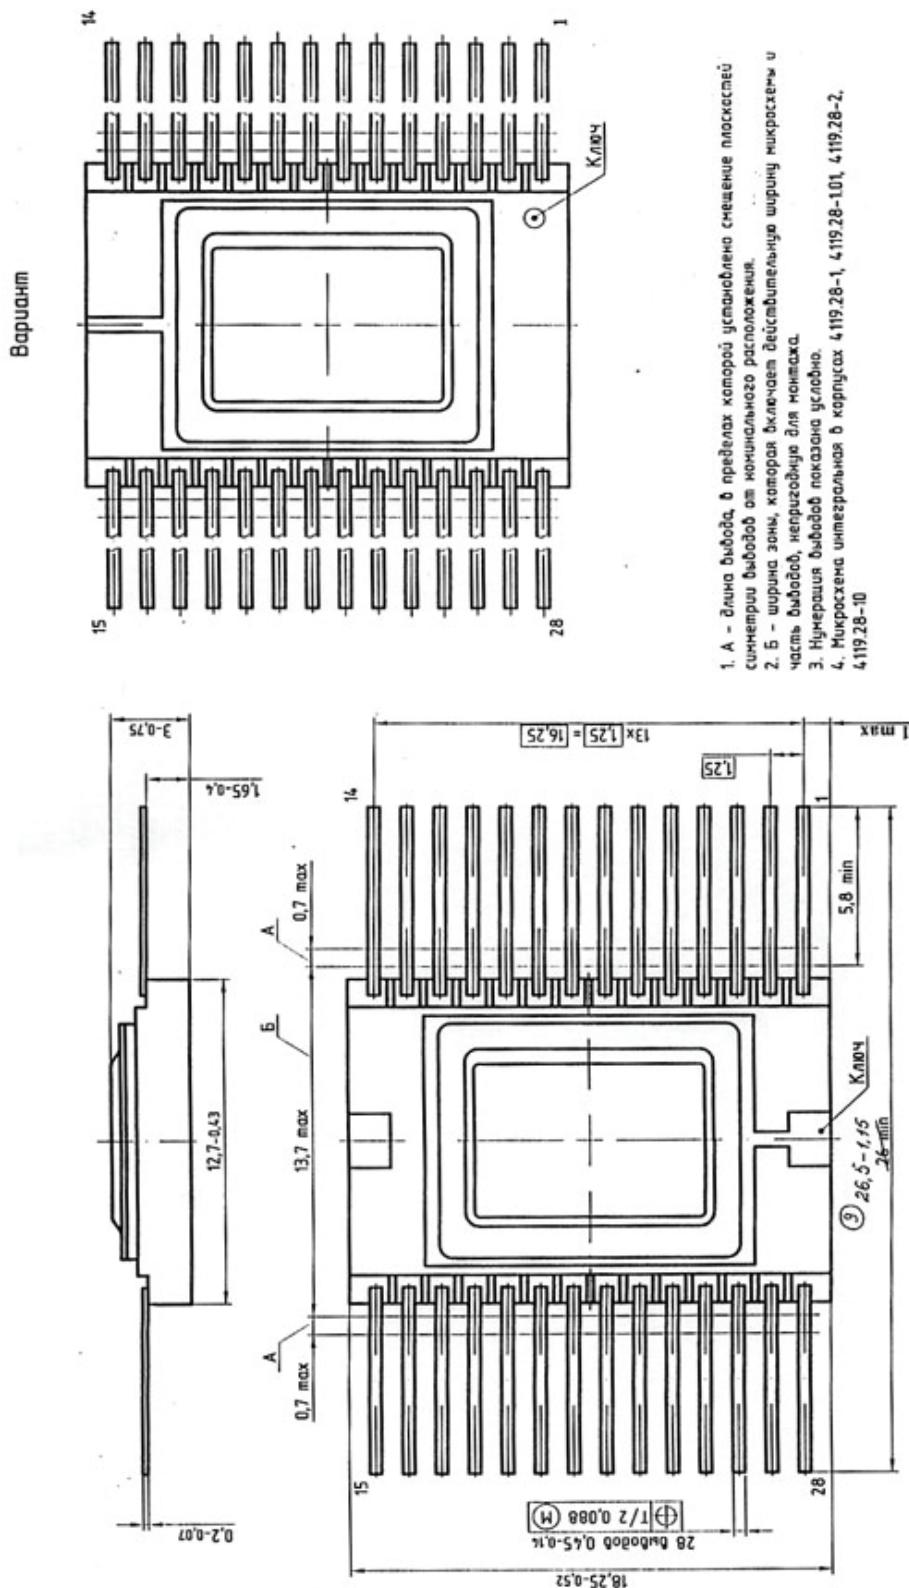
Габаритный чертеж корпуса 4119.28-1.01
